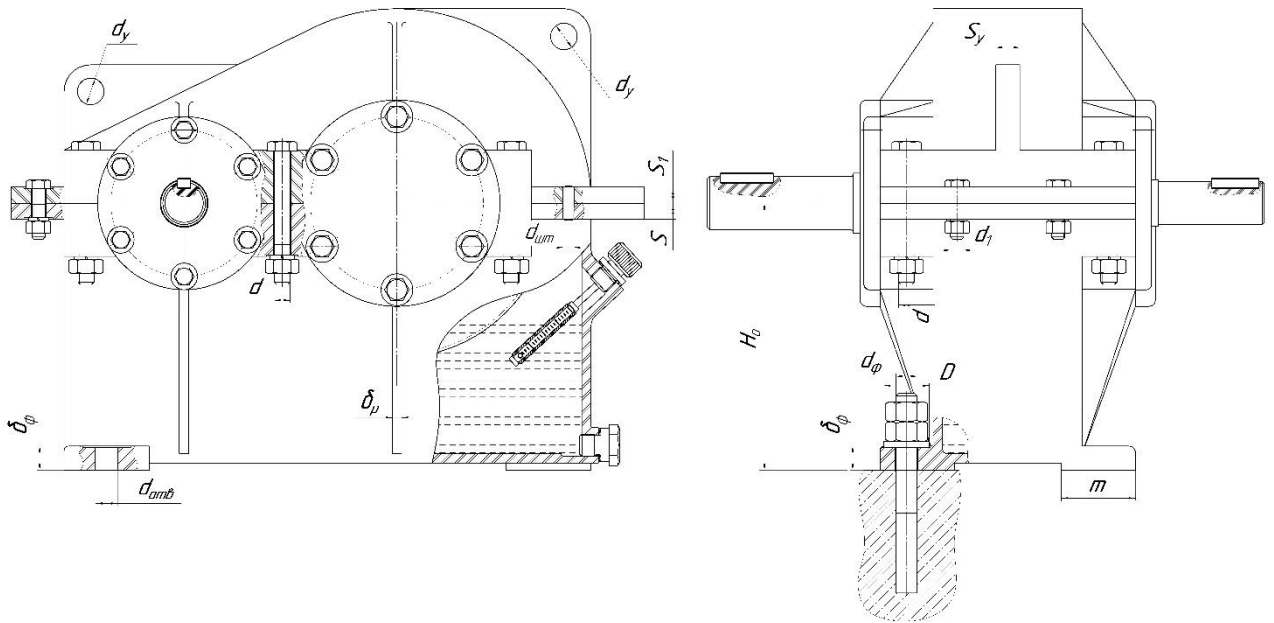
К определению рекомендуемых соотношений размеров корпуса редуктора
